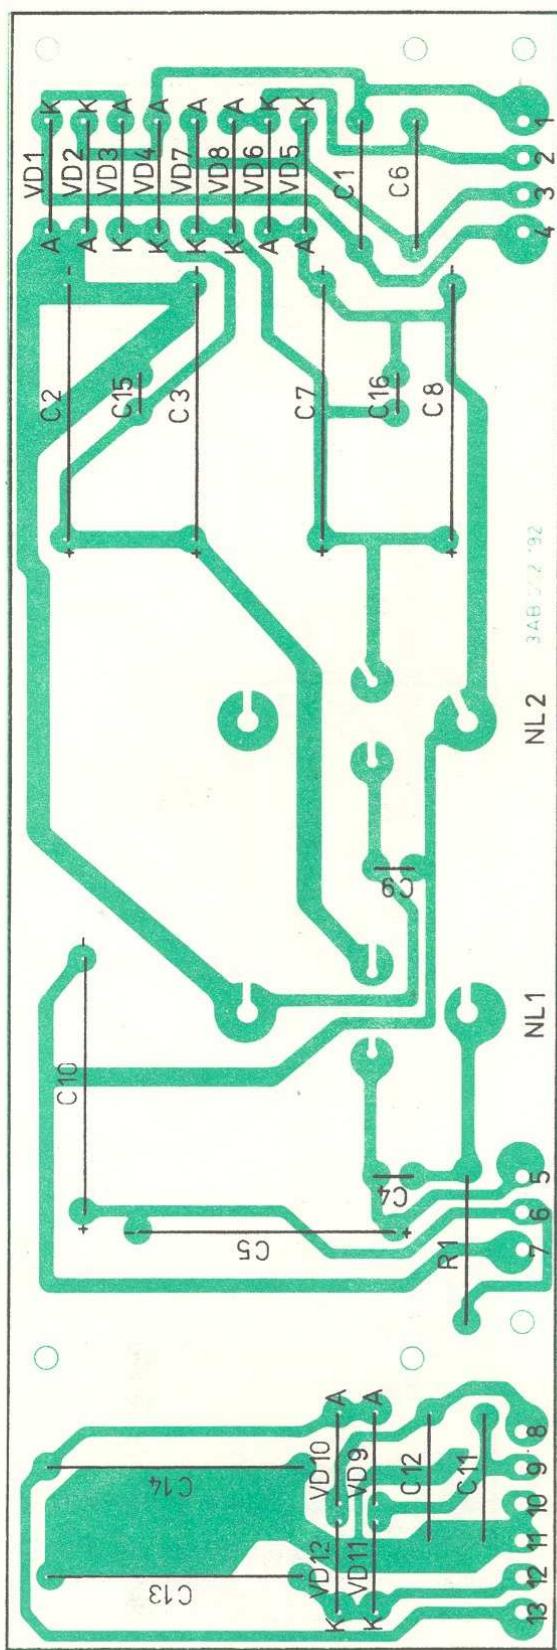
Deska indikátoru 3AK 054 159 (pohled ze strany spojů)
